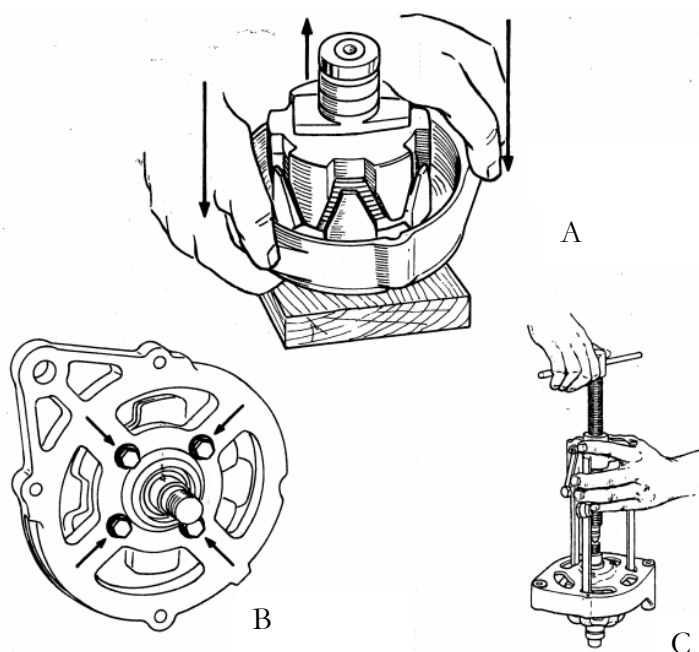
Separação da tampa de suporte frontal do alternador do rotor ([6]).
